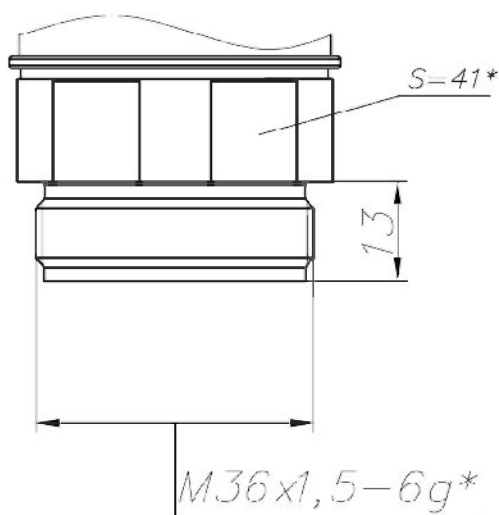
Габаритные размеры штуцера преобразователей с кодом присоединительной части А по таблице А.8
